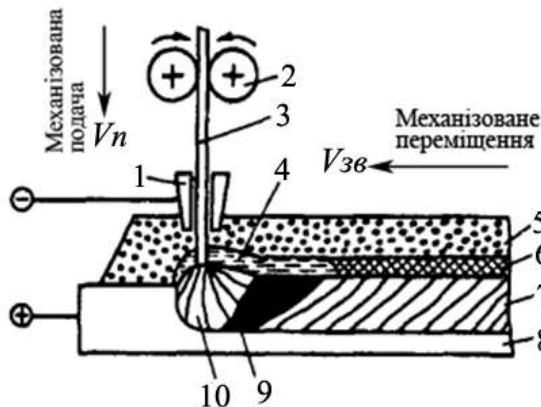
Схема автоматичного дугового зварювання під шаром флюсу
